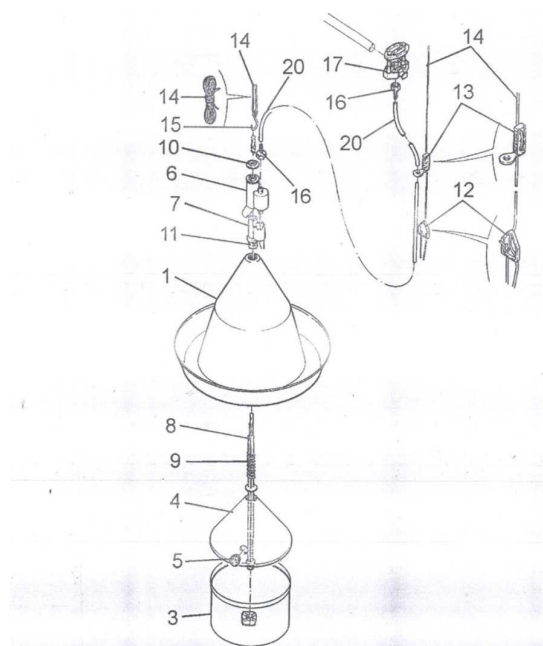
Круглая поилка: 1 – колокол поилки; 3 – нижняя часть поилки; 4 – крышка; 5 – заглушка; 6 – корпус клапана внешний; 7 – корпус клапана внутренний; 8 – подвесной стержень; 9 – пружина большая; 10 – контргайка; 11 – клапанное устройство; 12 – натяжное устройство для подвесного каната; 13 – направляющие шланги; 14 – подвесной канат; 15 – S-крюк; 16 – наконечник; 17 – заслонка; 20 – шланг
